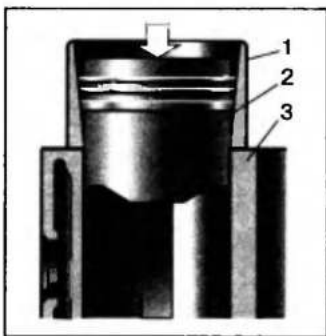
Установка поршня с кольцами и шатуном в цилиндр с помощью конической оправки: 1 — оправка; 2 — поршень; 3 — блок цилиндров
